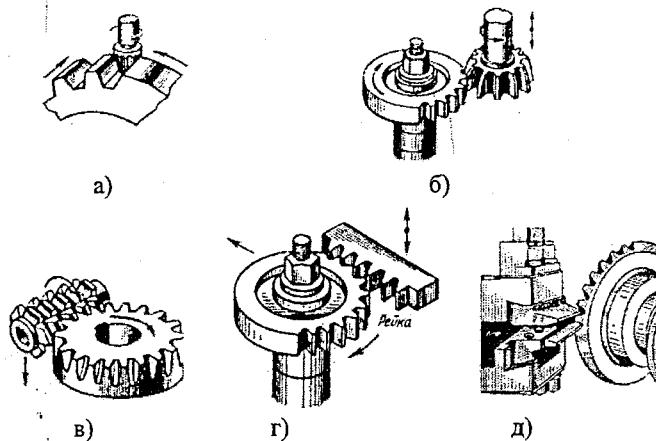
Способи виготовлення (*ways of producing*) зубчастих коліс
